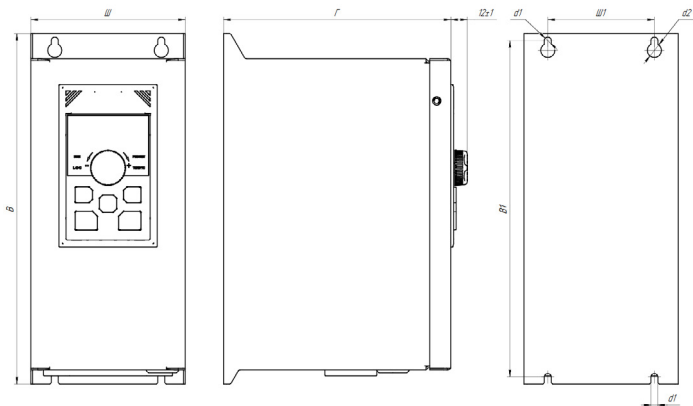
Установочные и габаритные размеры тормозного модуля BU, типоразмер 1
